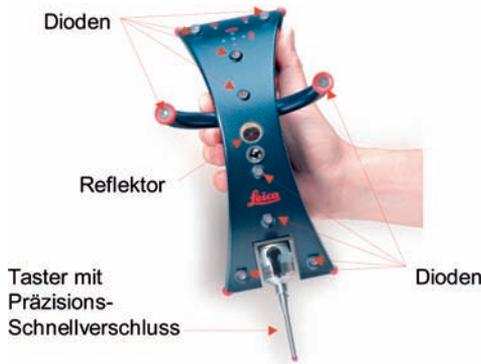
T-Probe, die handgeführte Koordinaten-Messmaschine.
